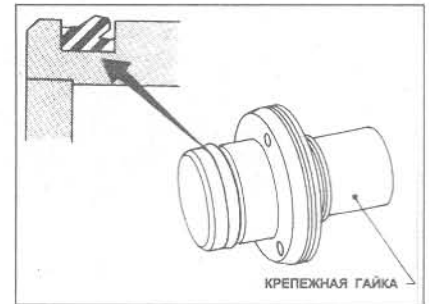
Правильная установка манжеты на крепежной гайке (Глава 25)
